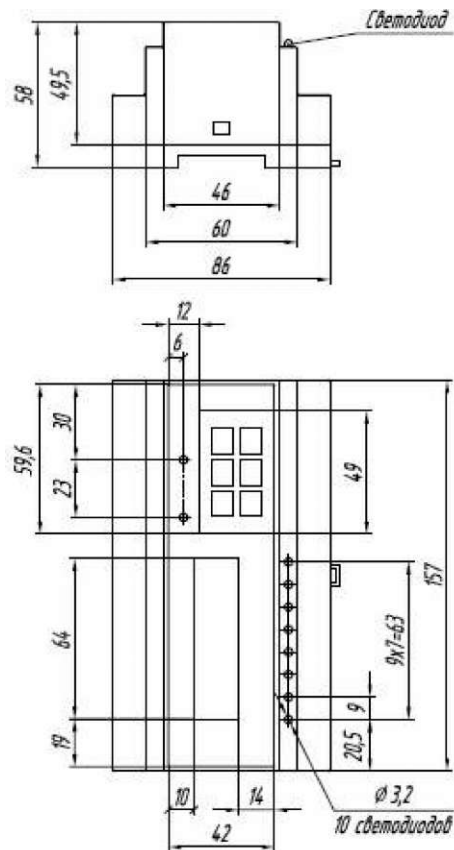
Габаритные размеры контроллера СГМ ЭРИС-130
